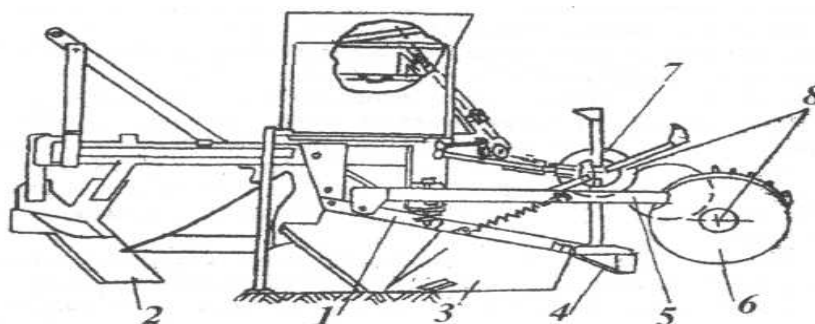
Схема приспособления лесопосадочного автоматического ПЛА-1 к плугу ПКЛ-70: 1 - неподвижная рама; 2 - черенковый нож; 3 - сошник; 4 - загортач; 5 - шарнирная рама; 6 - прикатывающие катки. 7 - посадочный аппарат; 8 - привод посадочного аппарата
